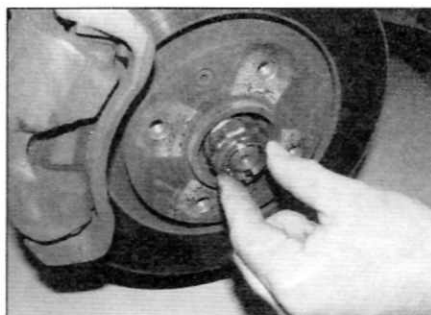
, б. ...и снимите стопорный колпачок с гайки крепления полуоси
